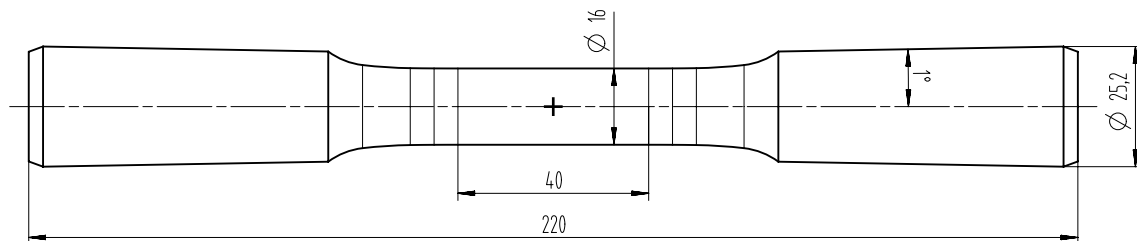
Fertigungszeichnung der Probengeometrie
